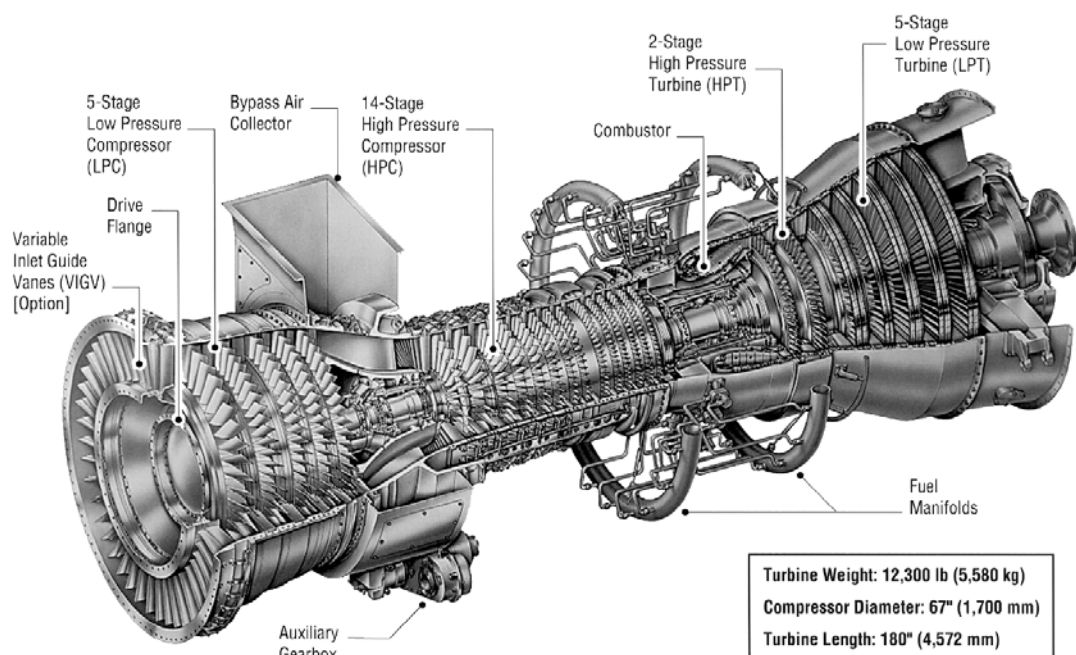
Sección de turbina de gas aeroderivada GE LM6000. Fuente: [17]
